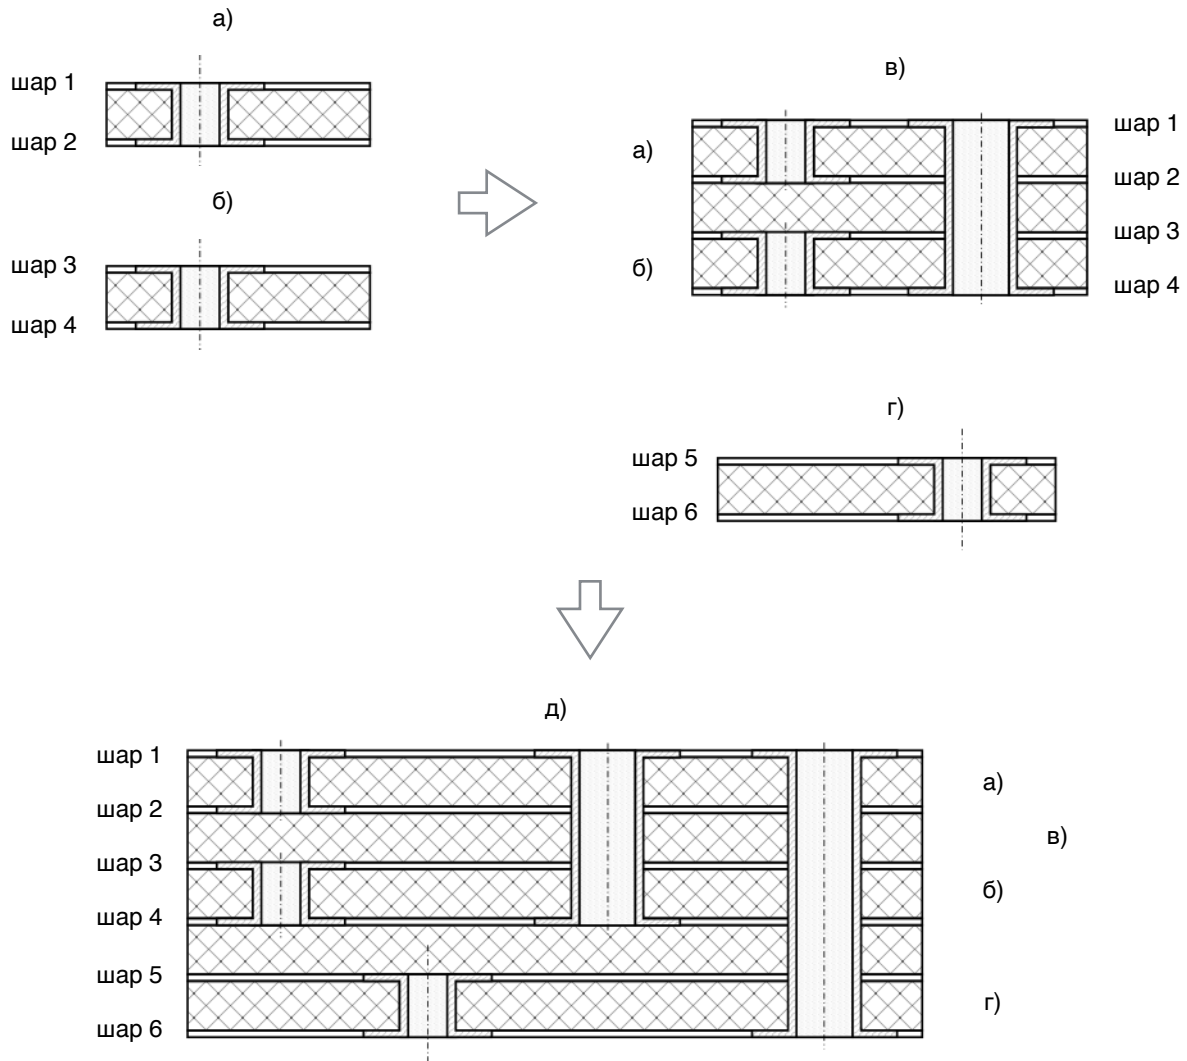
Схема виготовлення 6-ти шарової ДП
